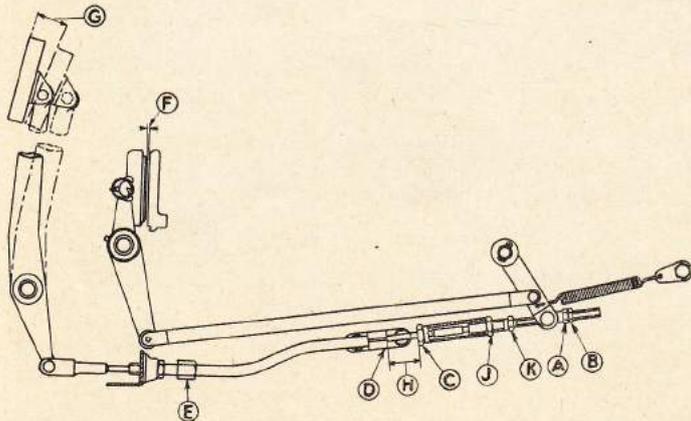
Commande d'embrayage : A : Ecrou de réglage ; B : Contre-écrou ; C : Ecrou de butée ; D : Butée ; E : Réglage ; F : Garde à la butée ; G : Garde à la pédale ; H : Garde à la butée (sur carter) ; J : Contre-écrou ; K : Tige de réglage.
